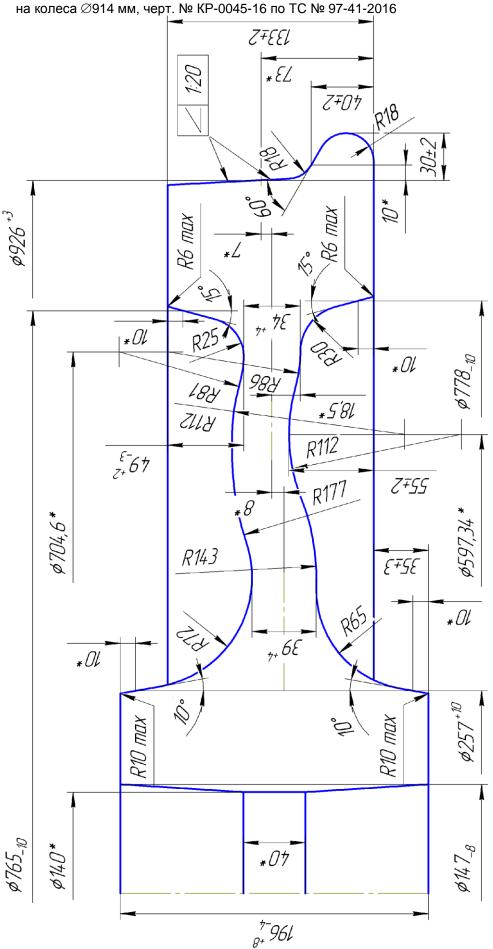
Колесо с черновой механической обработкой \varnothing 926 мм под чистовое ∅ 914 мм по чертеж № КР-0045-16 Масса 465 кг.
